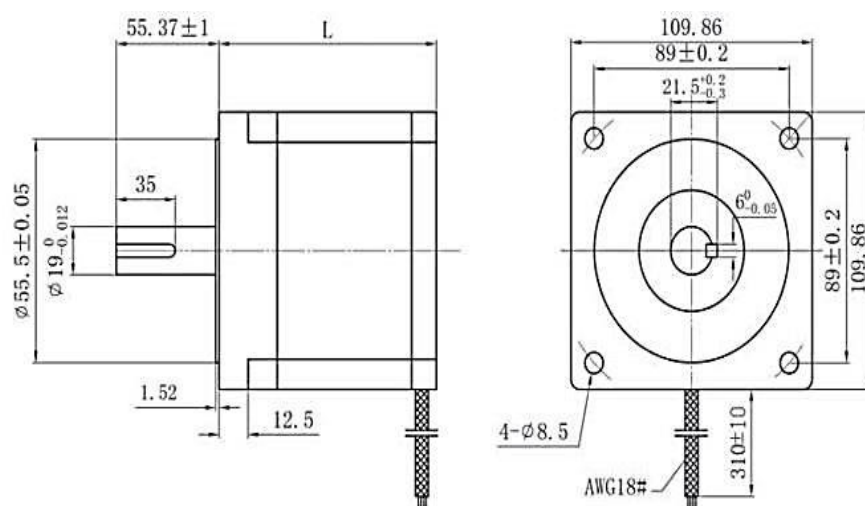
Размеры шагового двигателя FL110STH201-8004A
